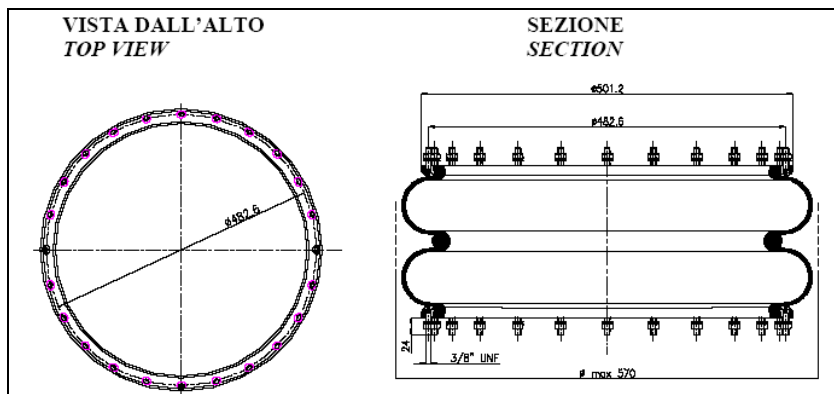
Pianta e sezione di air spring (rif. CF gomma, Milano)
